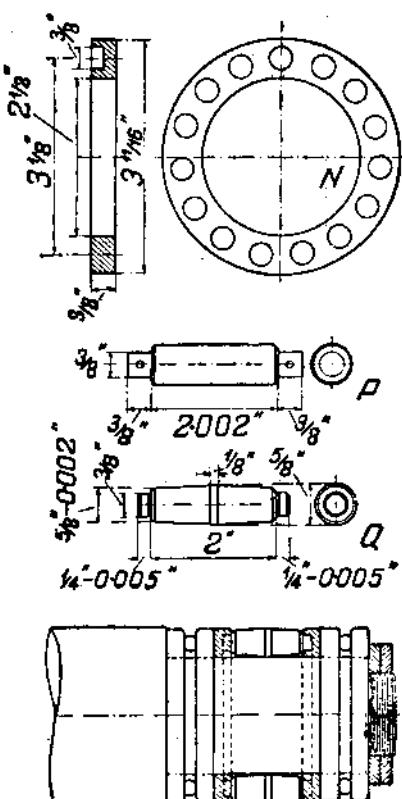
Вальцовка для цилиндров двигателей внутреннего горения.
